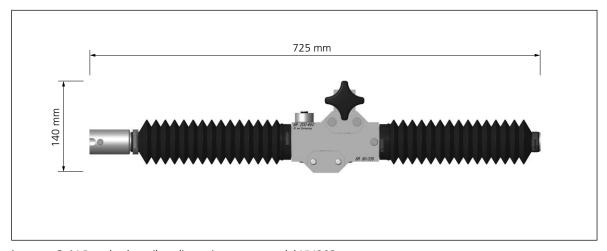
Vista desde arriba, dimensiones en mm del HV 203
